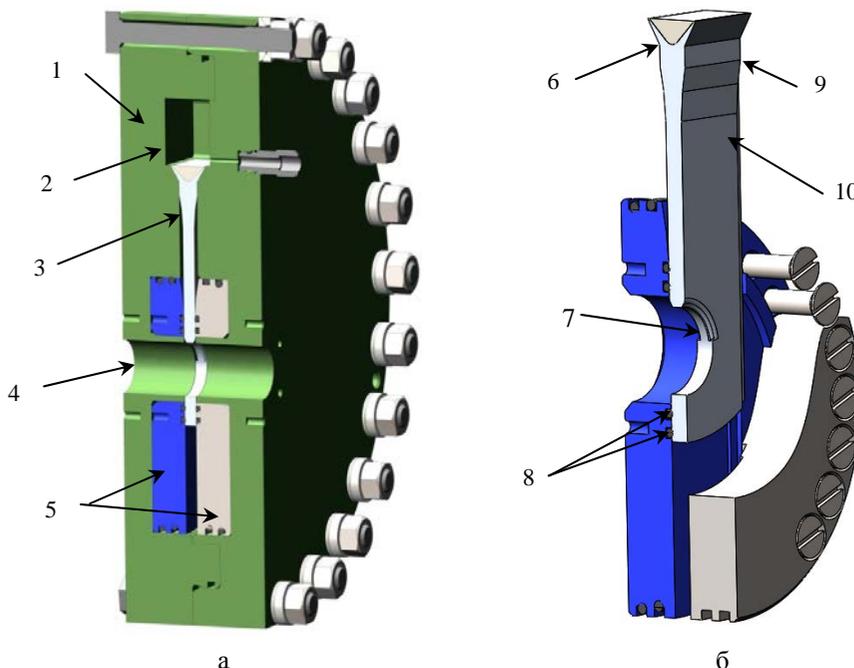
Опытный образец конструкции взрывозаслонки: а – общий вид в разрезе, б – внутренние обоймы и заслонка; 1 – внешний корпус; 2 – камера с нагружающим ВВ; 3 – Клиновидная заслонка (сплав В95, Д16 или сталь 12Х18Н10Т); 4 – отверстие проходное; 5 – внутренние обоймы; 6 – фланец «ласточкин хвост»; 7 – угловая радиусная выборка; 8 – уплотнения из резины марки НО-68-1 НТА; 9 – угловой клин на заслонке; 10 – уплотняемая поверхность
